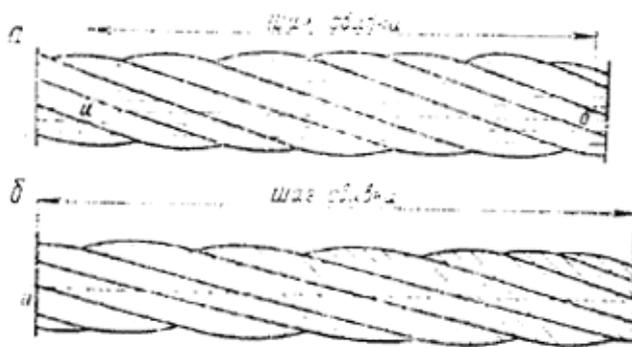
Определение шага свивки шестипрядного каната: а — крестовой свивки; б — то же, односторонней
